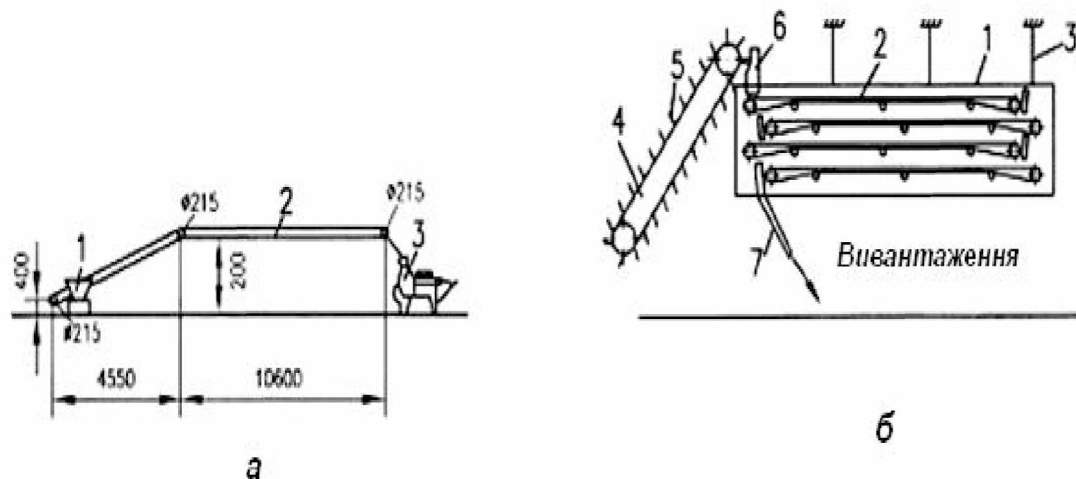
Обладнання для попереднього вистоювання: а – стрічковий транспортер: 1 – тістоподільна машина; 2 - транспортер; 3 – тістозакатна машина; б - стрічкова шафа: 1 - шафа для попереднього вистоювання; 2 - стрічкові транспортери; 3 - підвіски; 4 - ковшовий транспортер; 5 - ковші; 6 - лоток-розподільник; 7 - лоток для розвантаження.
